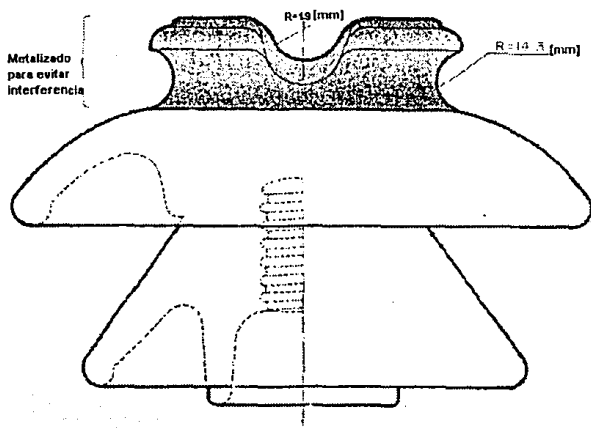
Aislador Tipo Alfiler A56-2.
